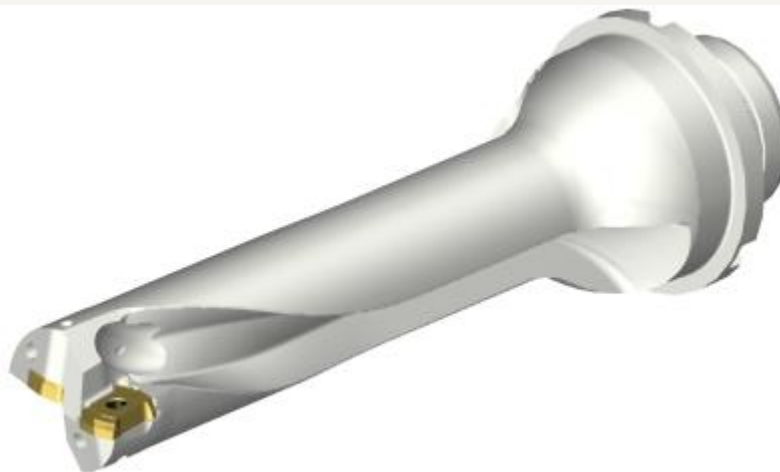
Розточна голівка з різцем для обробки кріпильних отворів
